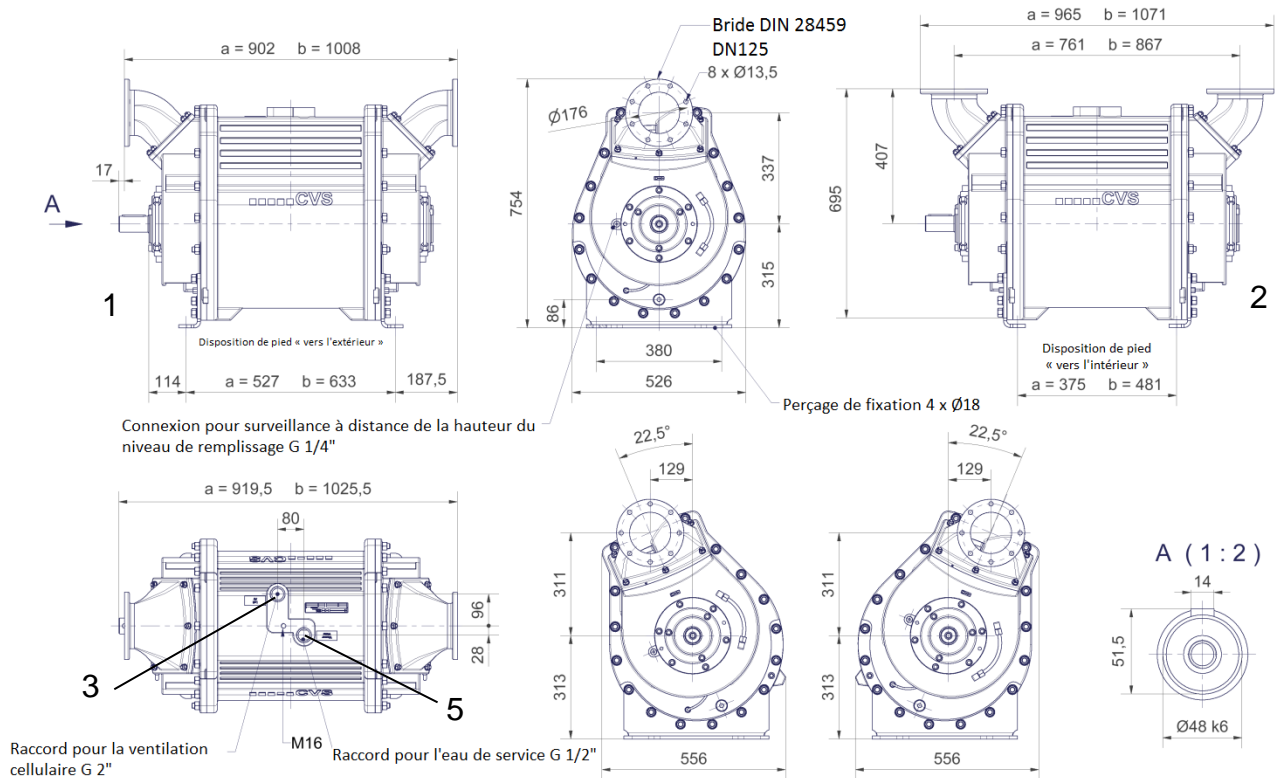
Dimensions de la VacuStar WR 2500 / WR 3100, la WR 3100 est représentée
